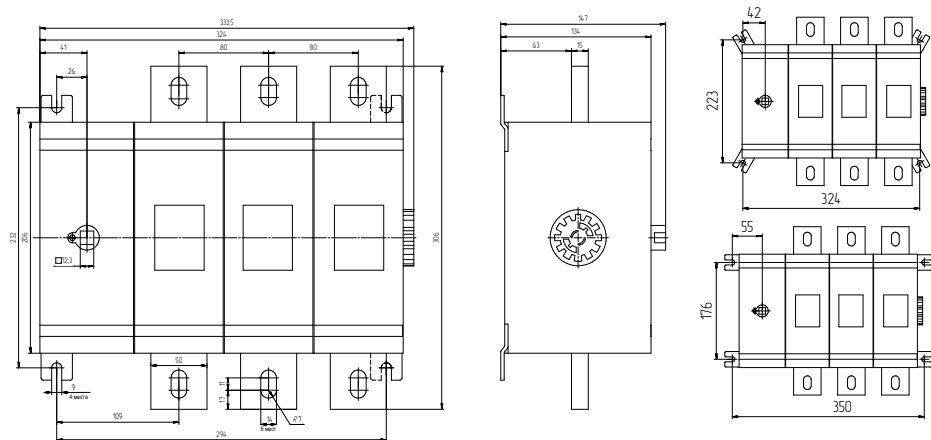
Выключатель-разъединитель 1000 – 1250 А стандартного исполнения
